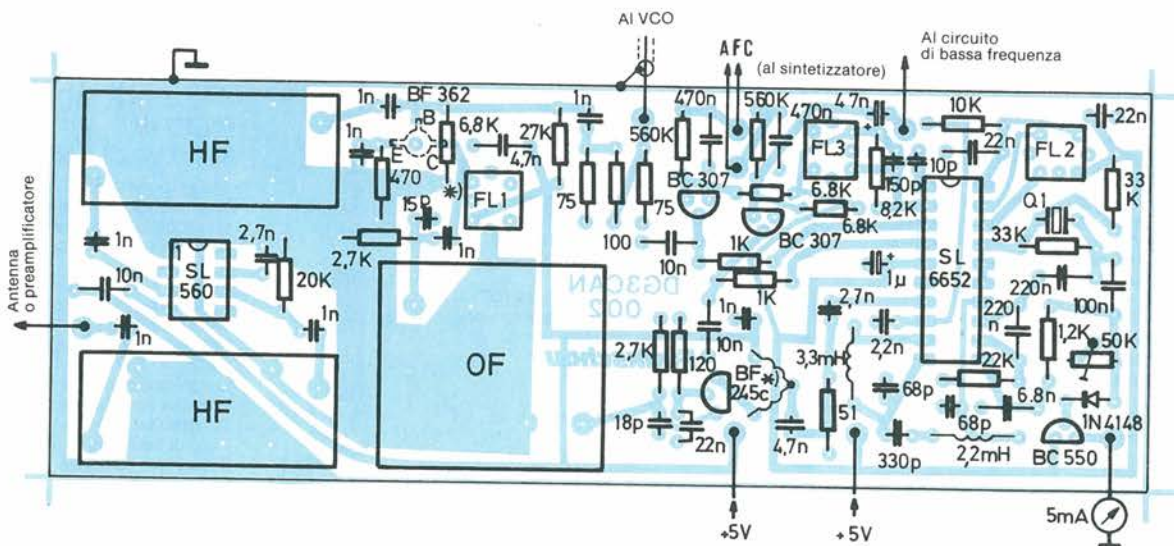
Disposizione dei componenti sullo stampato della parte ricevente: il BF362 deve essere saldato sulla parte inferiore.
